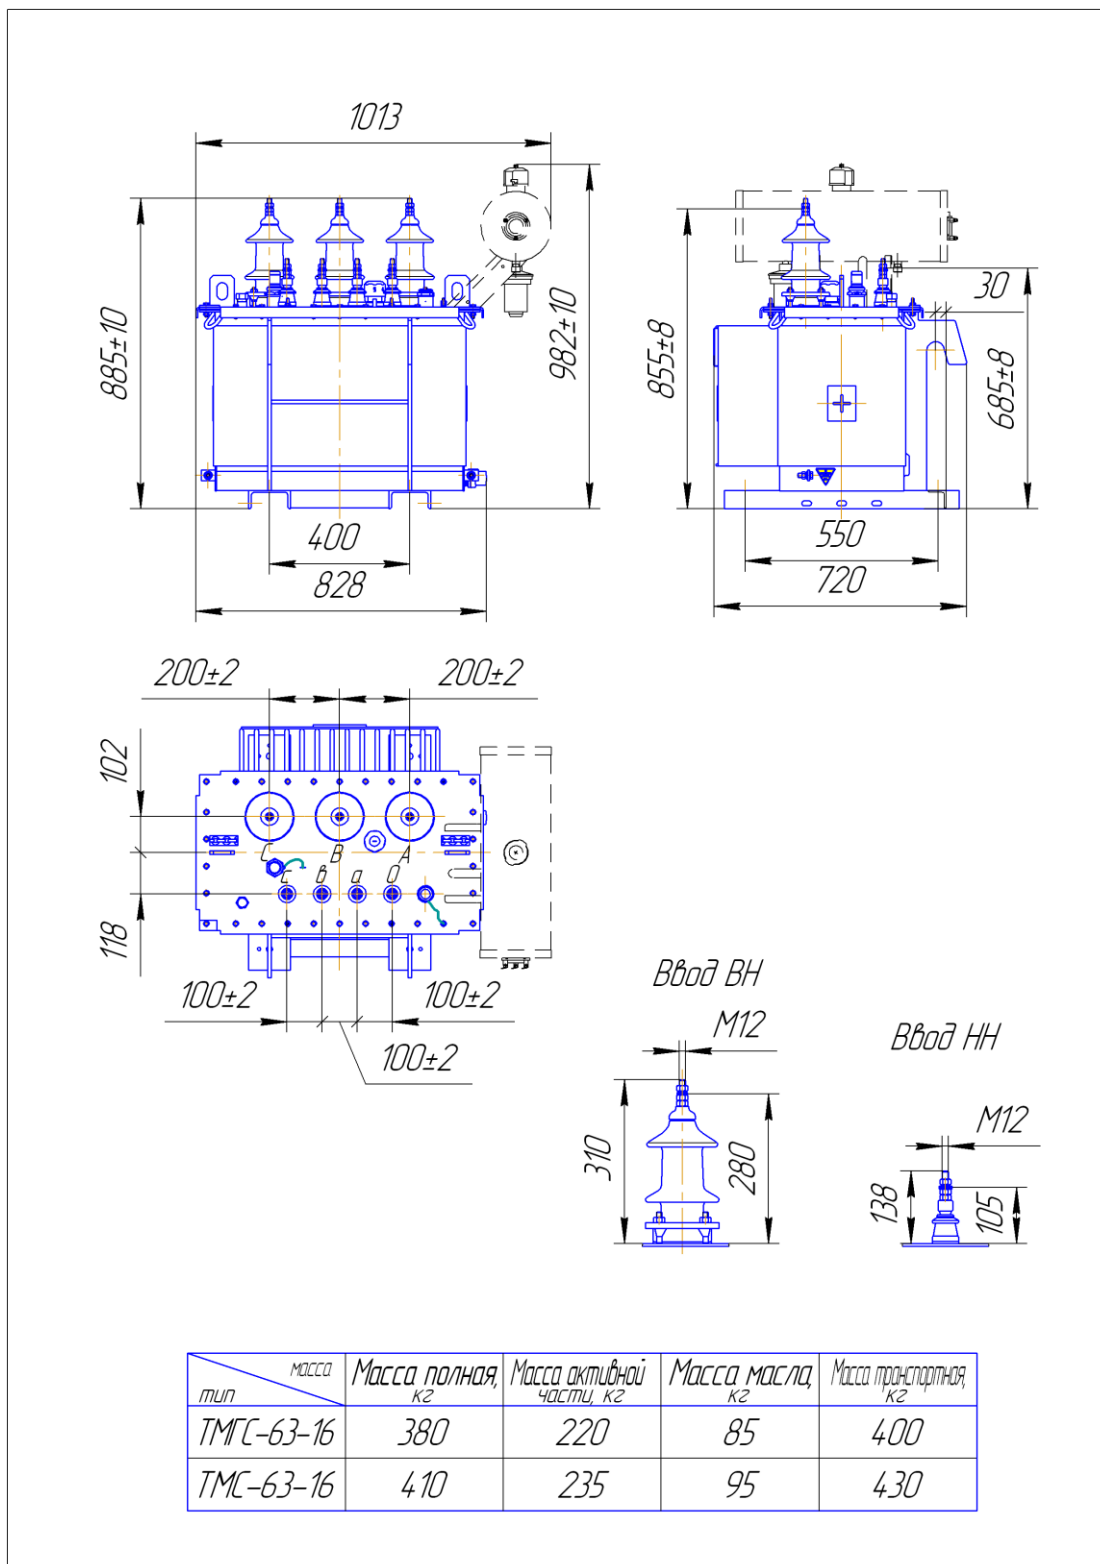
Габаритные, установочные и присоединительные размеры трансформатора ТМГС - 63/10-16
